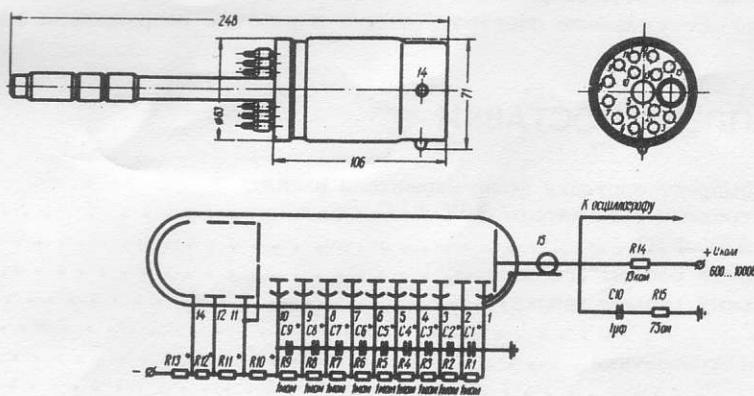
Габаритные размеры, цоколевка и схема включения прибора типа ЭЛУ-ФТС
